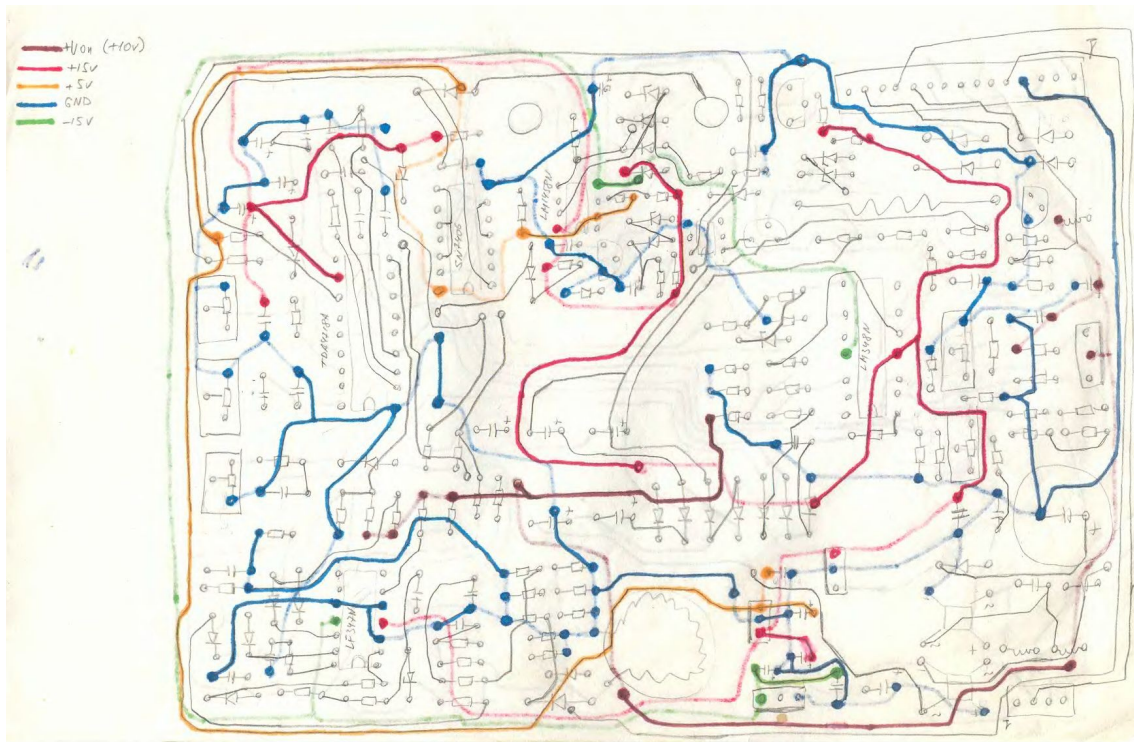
Зарисовка платы управления сварочного источника RytmArc со стороны компонентов.
